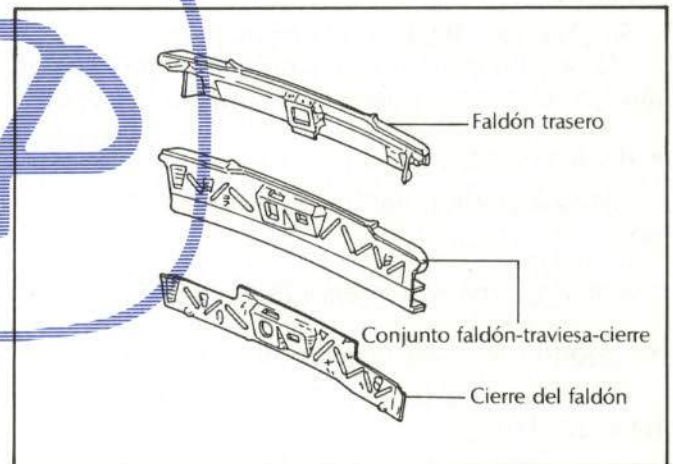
Comercialización del conjunto faldón-traviesa-cierre.
